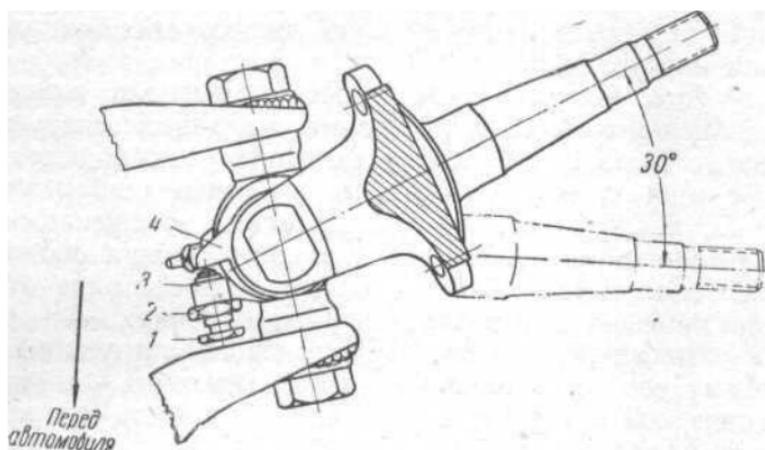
Регулировка угла наибольшего поворота стойки подвески автомобиля модели 407:
